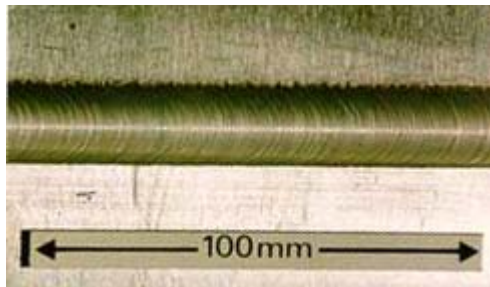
Schema di giunzione mediante Friction Stir Welding (fonte: The Welding Institute, 2000)
